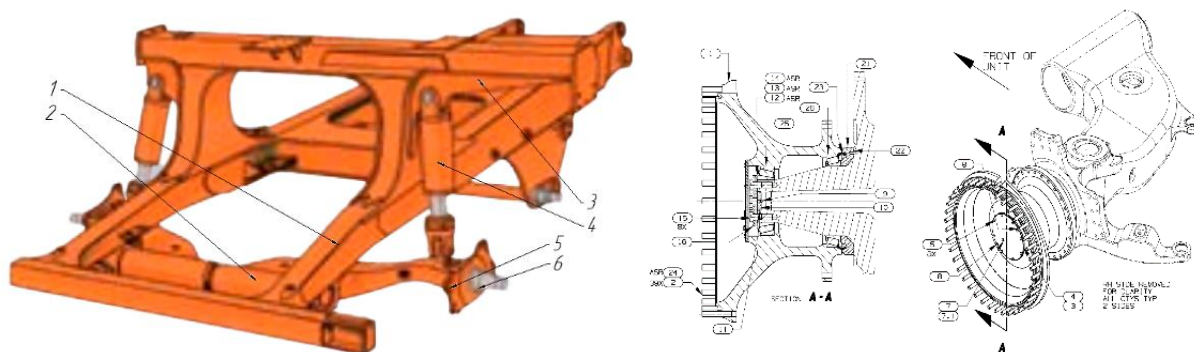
Конструкция передней подвески Hitachi EH 4000. 1 – рама; 2 – продольный рычаг; 3 – верхняя балка; 4 – ПГР передней подвески; 5 – шкворневой механизм; 6 – ступица
